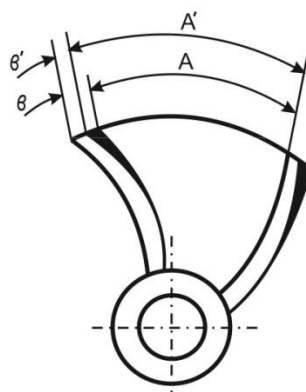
Схема подрезки рабочего колеса по лопаткам [10]
